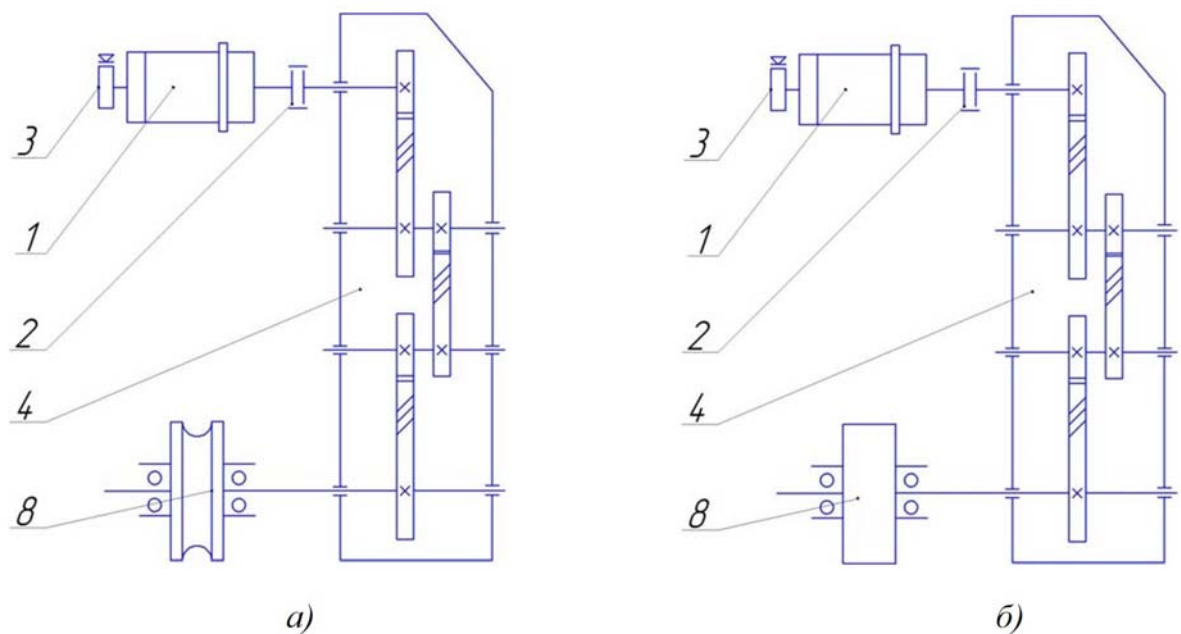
Кінематична схема механізму пересування крана: а) до модернізації; б) після модернізації : 1 - двигун; 2 - муфта; 3 - гальмо; 4 - редуктор; 8 – ходове колесо
